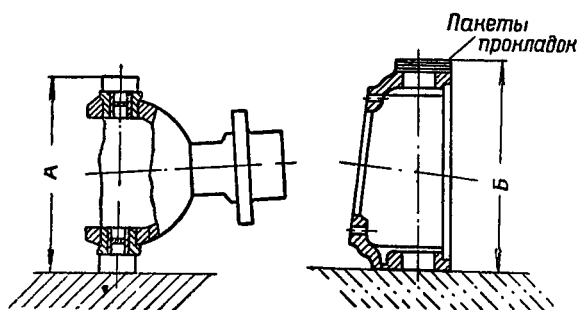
Подбор прокладок при регулировке шкворневых подшипников
